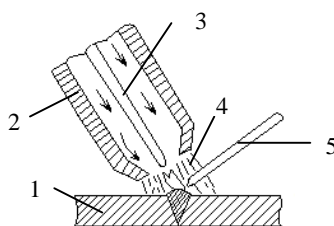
Схема аргонодуговой сварки:
